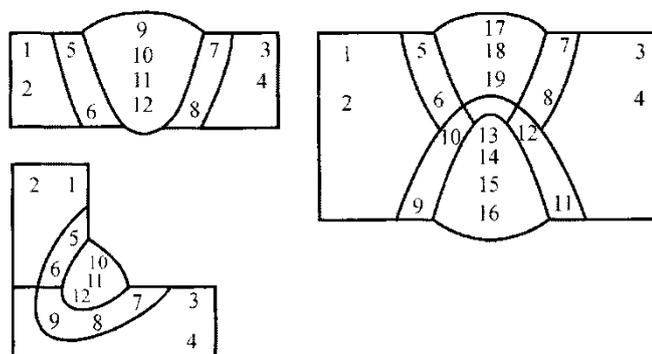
Схемы порядка замеров твердости на участках сварного соединения
